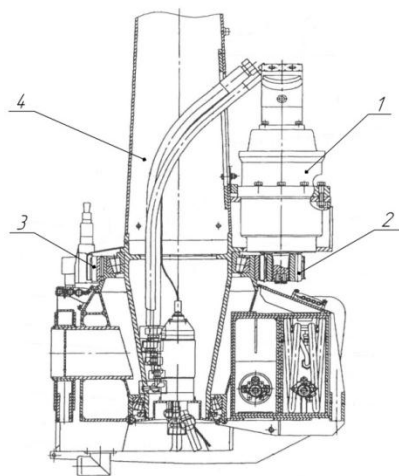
Опорно-поворотний пристрій на основі гідромотора та циліндричної передачі.
